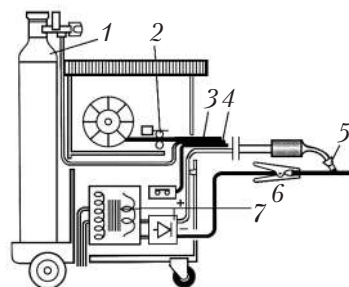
Установка для напівавтоматичного зварювання в захисному газі:
